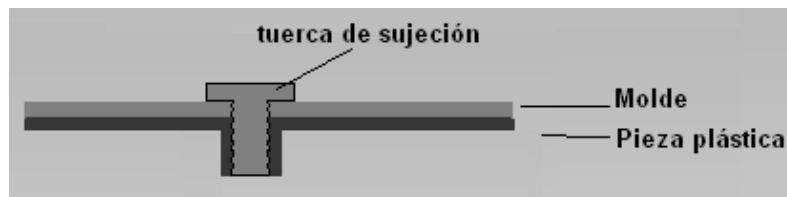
Rosca manufacturada durante el proceso de rotomoldeo mediante la adición de un elemento extra al molde.
